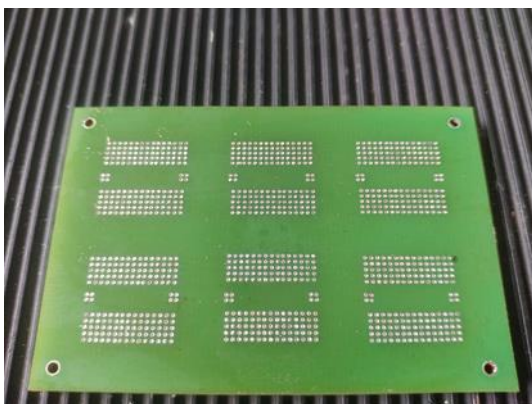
PCB-Substrat mit SAC-305-Via-Filling
